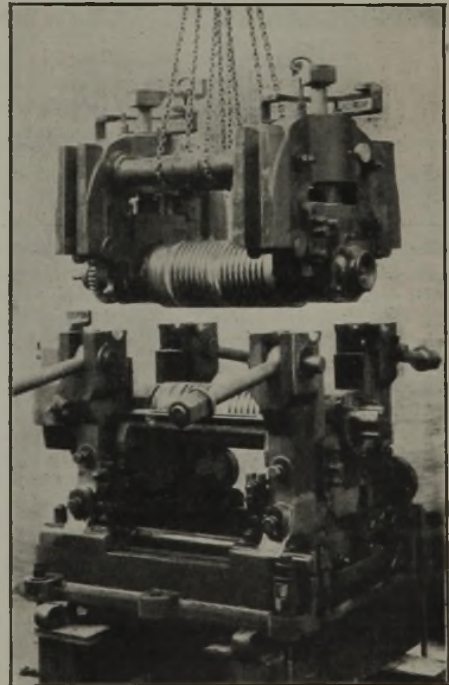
Walzgerüst mit abhebbarer Oberwalze im geteilten Gerüst.
